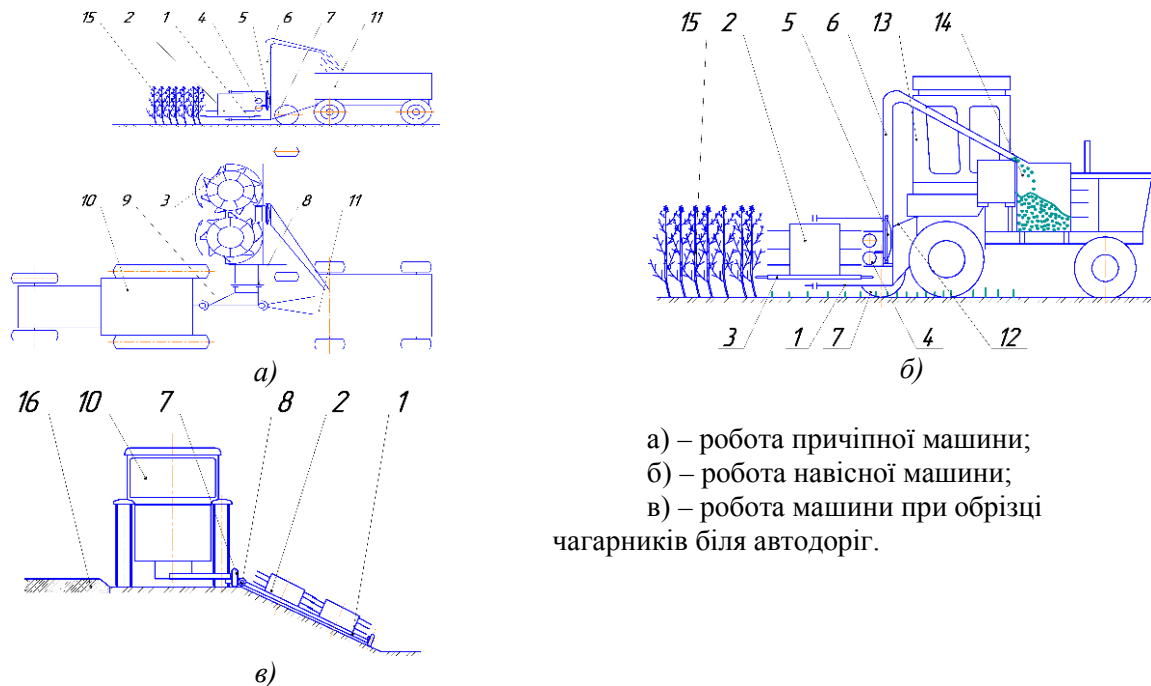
Схема роботи проектної машини: 1 – рама; 2 – направляюча; 3 – дисковий ножовий апарат; 4 – вальці прижимні; 5 – подрібнювач; 6 – дефлектор; 7 – опорне колесо; 8 – шарнірний пристрій; 9 – причіпний пристрій; 10 – трактор; 11 – причеп 2 ПТС – 4; 12 – навісний пристрій; 13 – косарка КПС – 5Г; 14 – бункер накопичення подрібненої маси; 15 – чагарники; 16 – автомобільна траса
